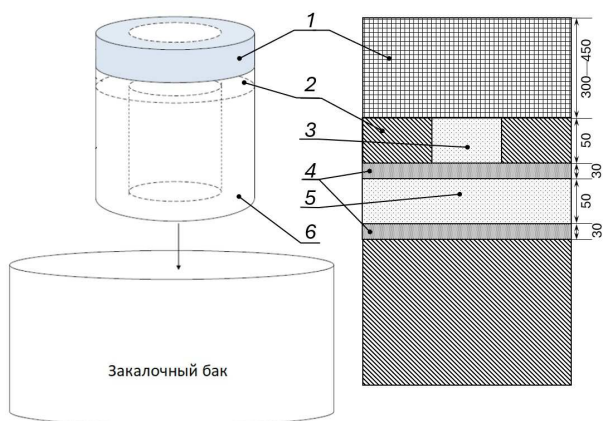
Схема проведения термической обработки заготовки под обечайку и расположение мест вырезки пробного кольца и образцов для сдаточных испытаний: 1 — тепловой барьер; 2 — пробное кольцо; 3 — место вырезки образцов для сдаточных испытаний; 4 — толщина реза; 5 — кольцо для изготовления образцов-свидетелей; 6 — заготовка под обечайку
